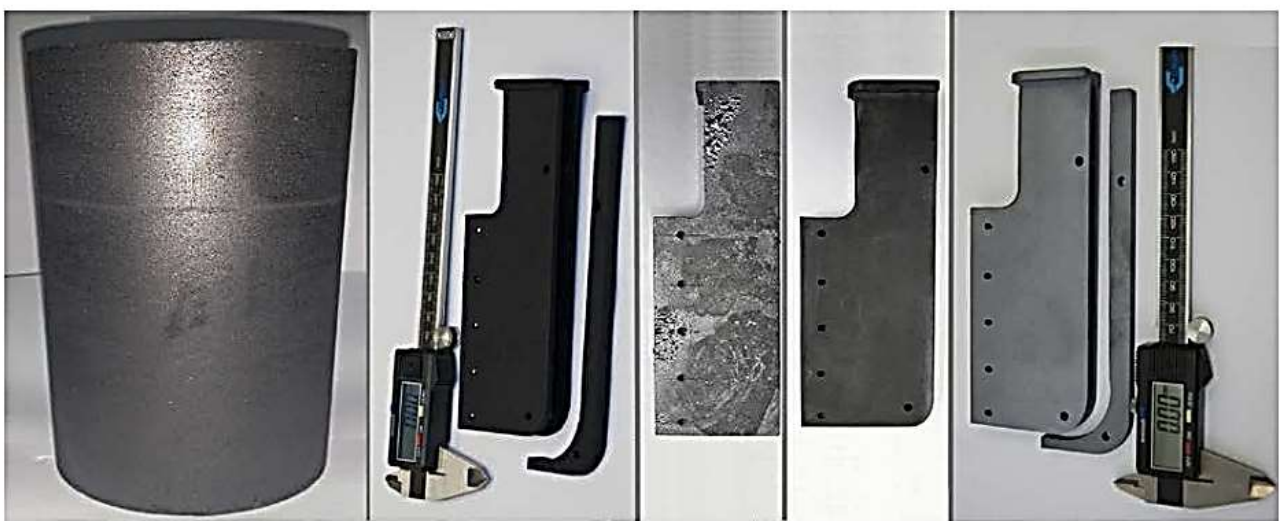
Этапы изготовления керамической карбидокремниевой детали для работы в высокоскоростном газовом потоке при температуре более 1500°C . Слева направо: болванка из углеродной пористой матрицы; углеродная заготовка после механической обработки; керамическая заготовка после силицирования; керамическая деталь после финишной обработки; деталь с нанесенным защитным SiC покрытием.
